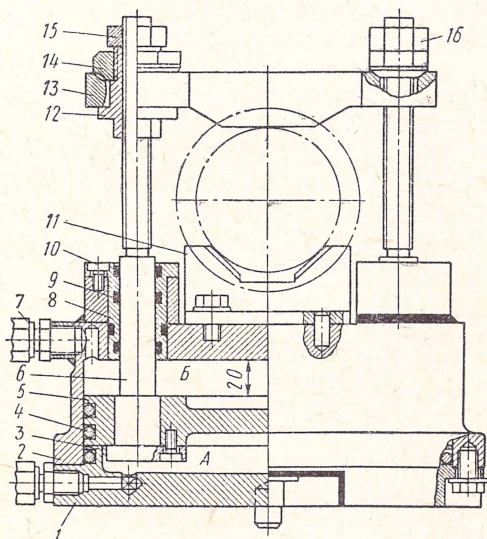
Пневмозажимное приспособление к фрезерному станку для закрепления круглых деталей
